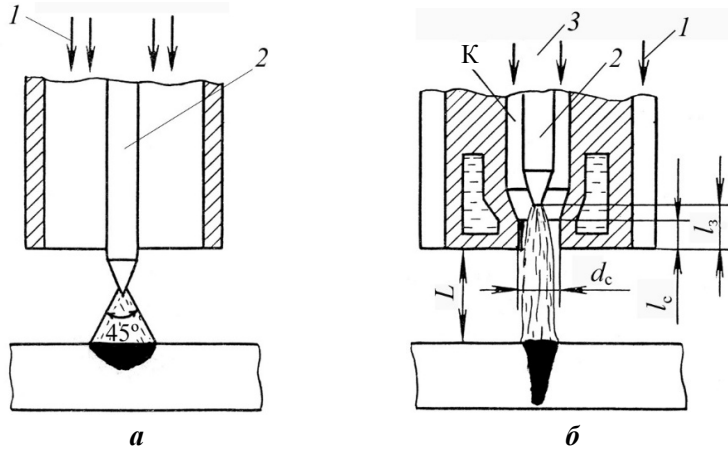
Схеми соплової частини пальника для електродугового (*a*) та плазмового (*б*) зварювання:
